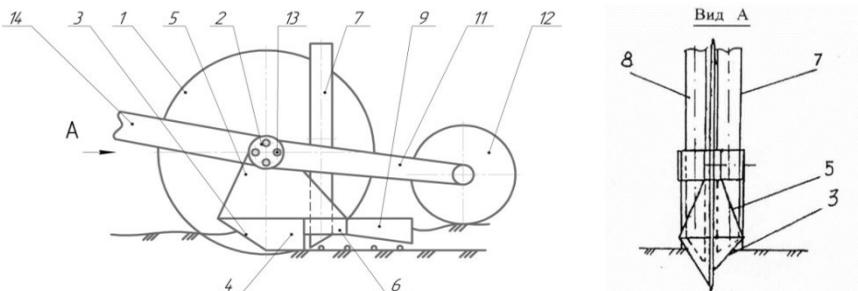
Комбинированный сошник зернотуковой сеялки
